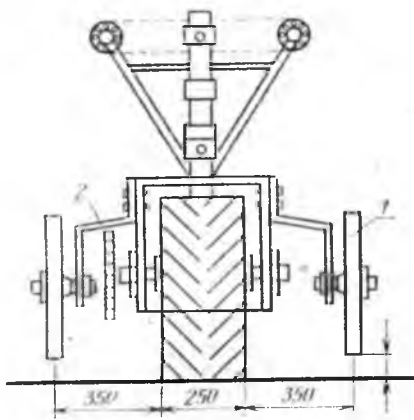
Вид спереди (без двигателя и редуктора). 1—дополнительные колеса; 2—кронштейны дополнительных колес
